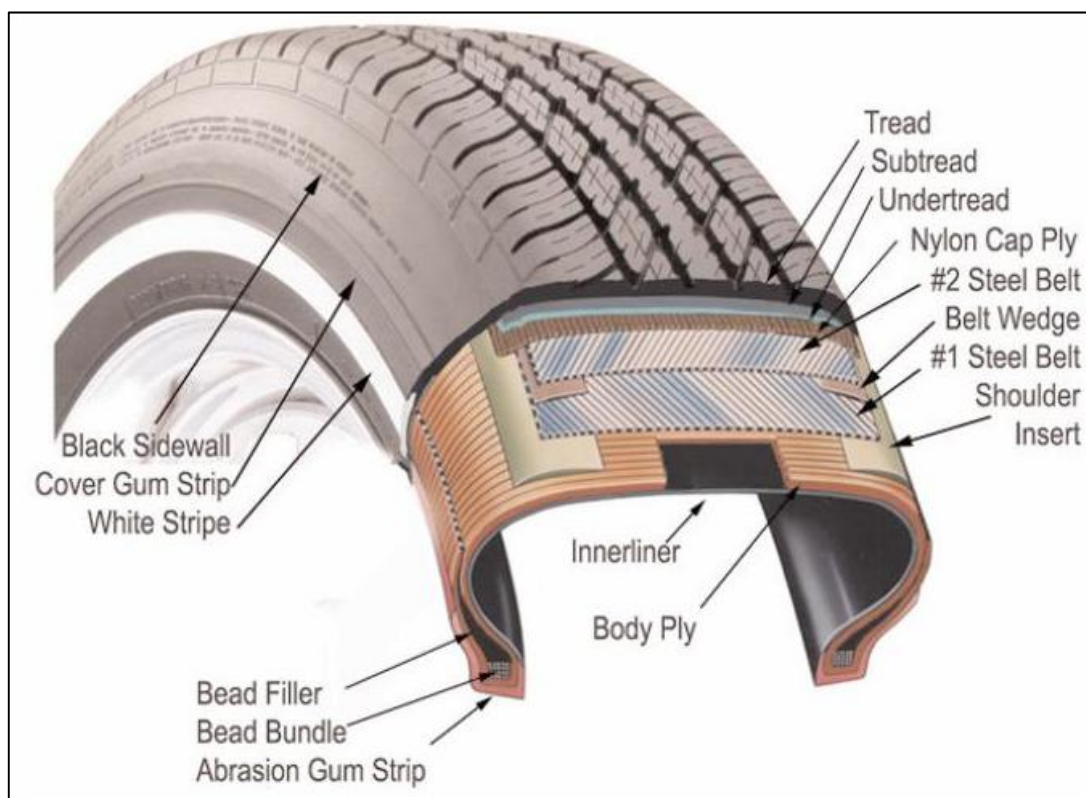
Struttura di un moderno pneumatico passenger
